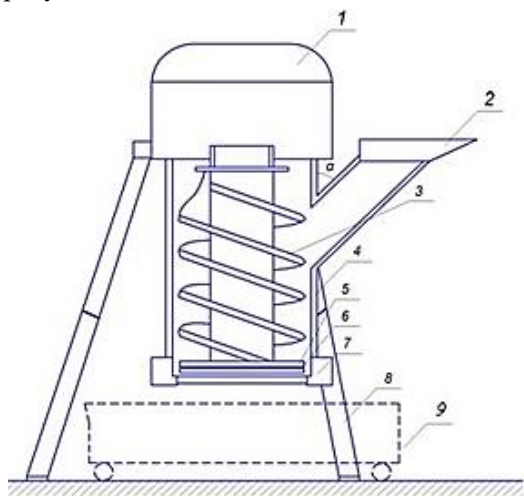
Мясорубка с вертикальным расположением шнека 1 – электродвигатель; 2 – загрузочная чаша; 3 – шнек; 4 – корпус; 5 – нож; 6 – решетка; 7 – прижимная гайка; 8 – ножки; 9 – тара для готового продукта (фарша)
